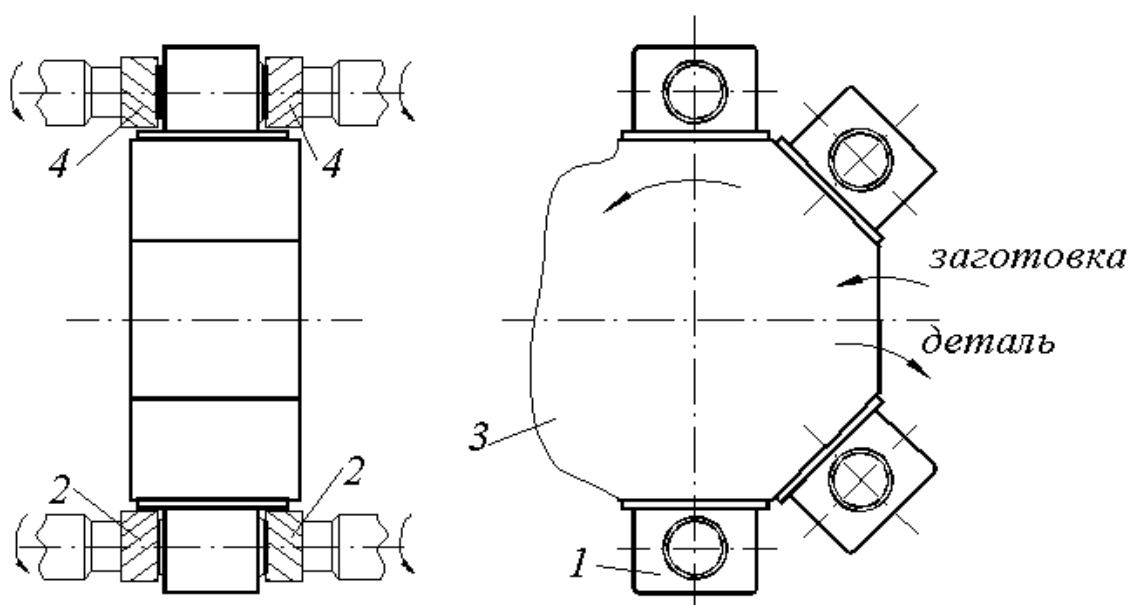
Схема обработки на барабанно-фрезерном станке
